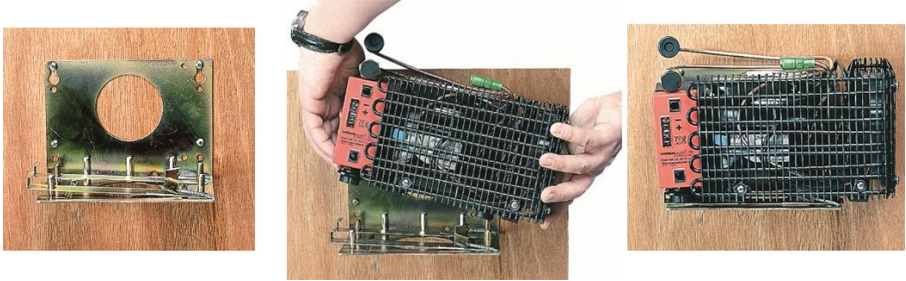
Деталь крепления компрессорного блока - кронштейна
